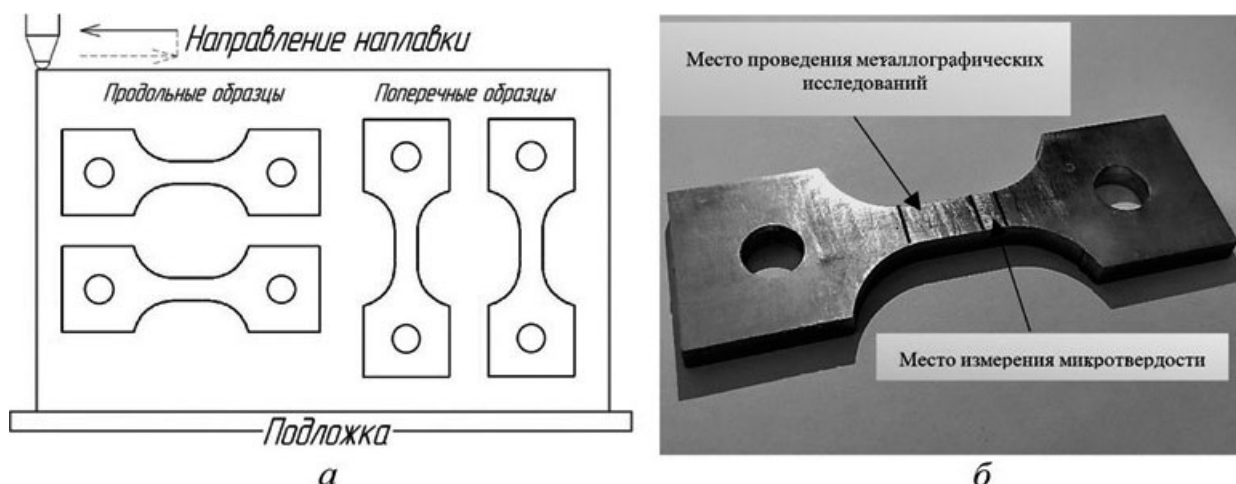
Схема вырезки образцов из наплавленной стенки (а) и их внешний вид с исследуемыми зонами (б)
